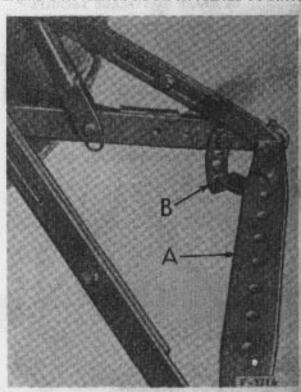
Barre d'attelage pour attelage 3-Points. À - Barre d'attelage. B - Plaquette de rigidité.
